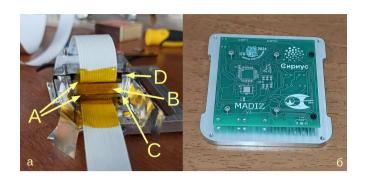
a — Сборка камер перед закрытием фольгой (A — камеры, B — проставка, C — крышка корпуса, D — основание корпуса); δ — вычислительная часть
